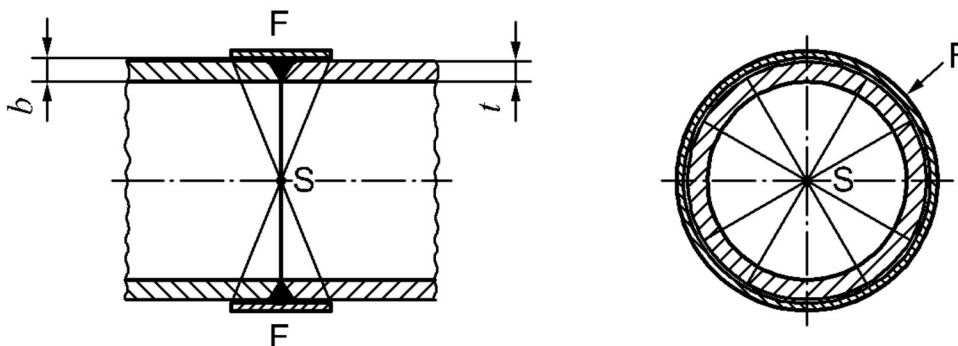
Схема контроля сварных швов с расположением источника излучения в центре трубы (панорамный контроль) и пленкой снаружи
